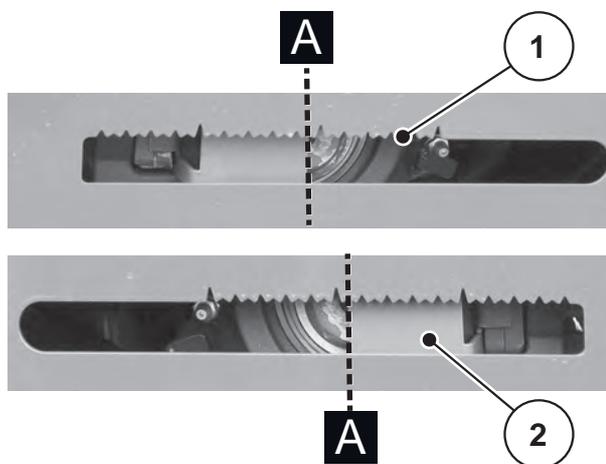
Регулировка пакетов тарельчатых пружин
